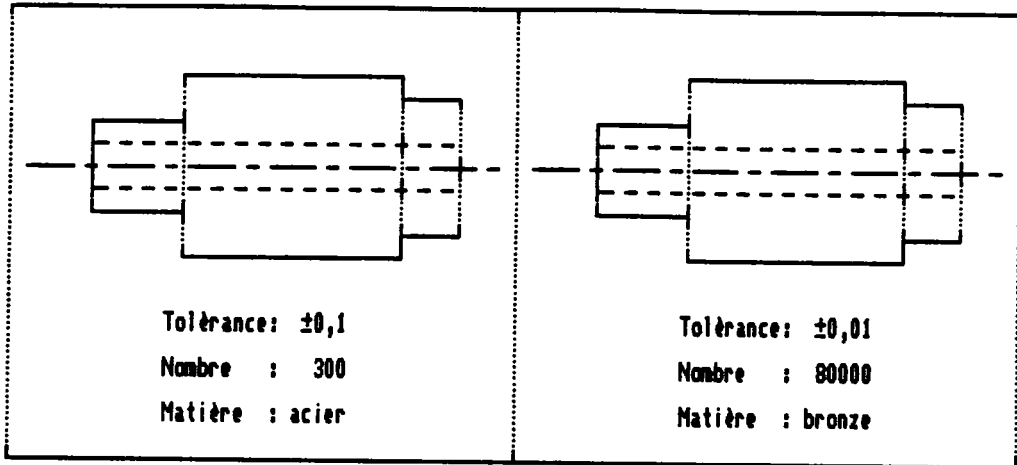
Pièces de formes et dimensions identiques mais de fabrication différente.
